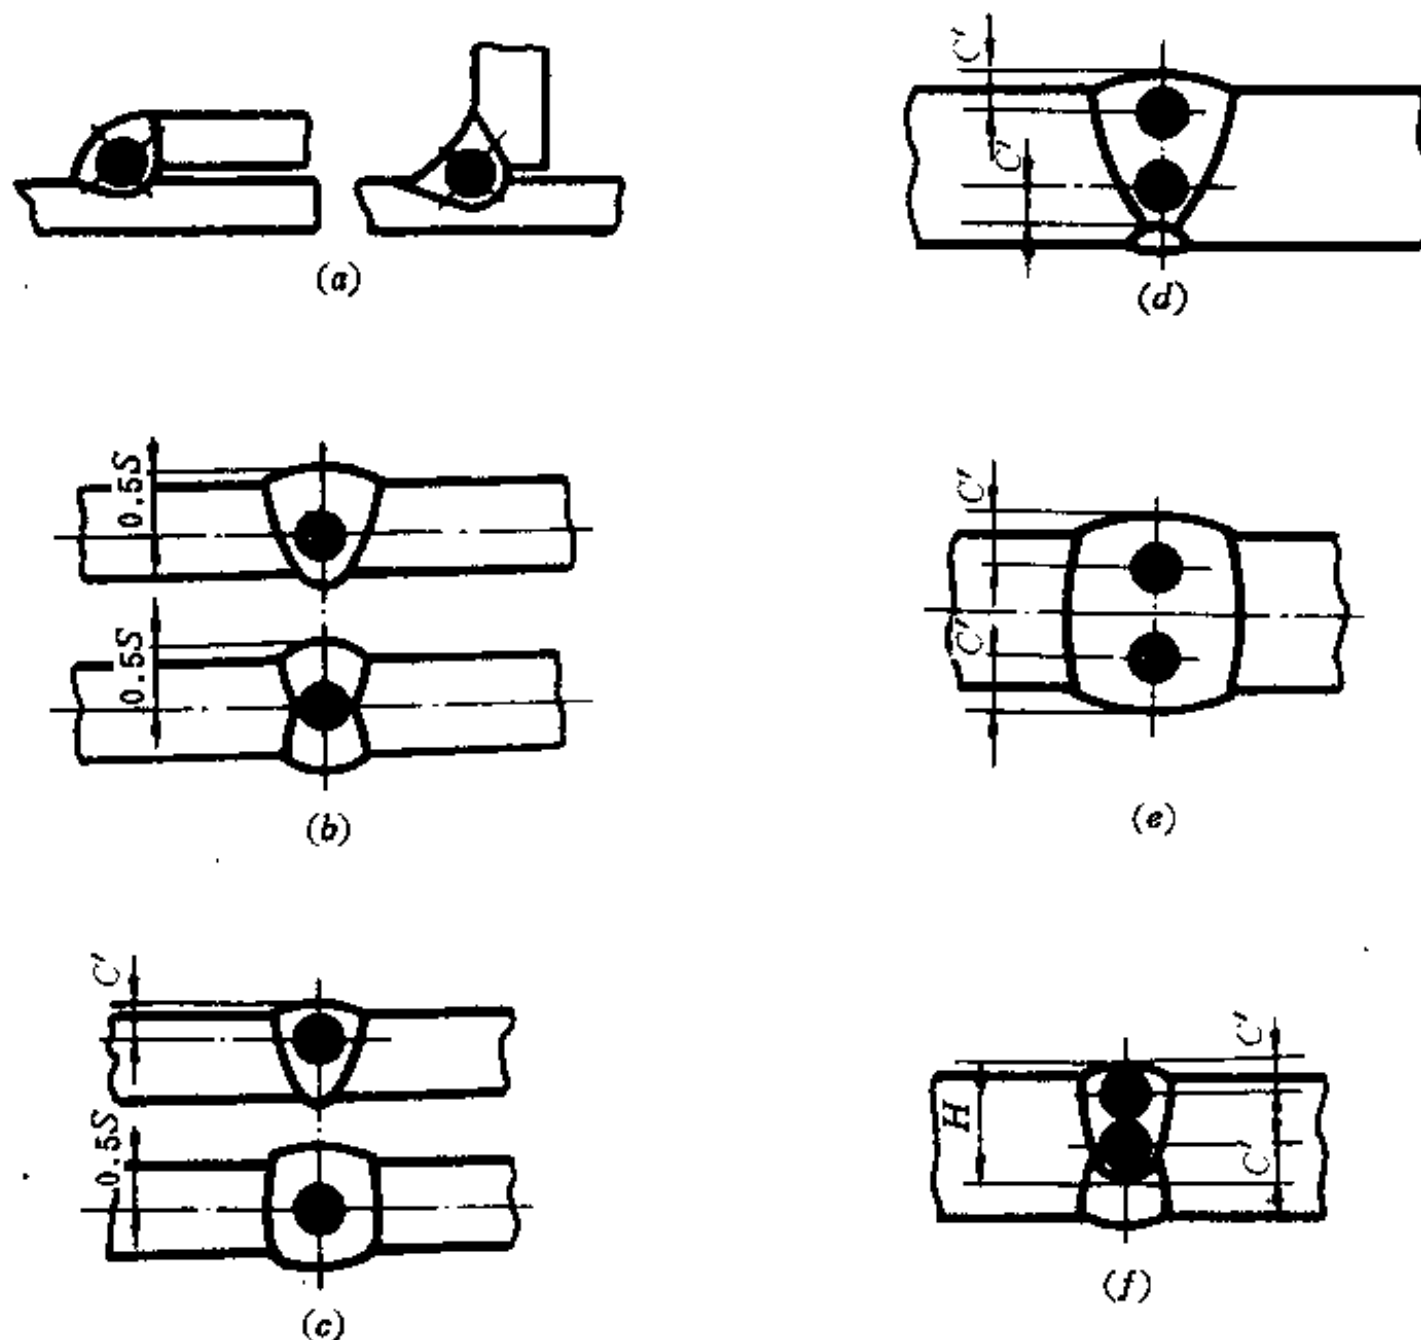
焊缝金属拉伸样坯的截取方法
